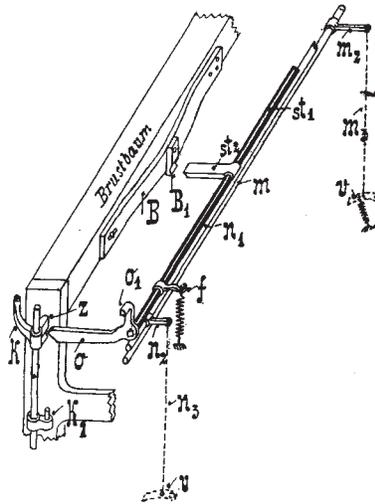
Ausrückung an Buckskestühlen durch die Bufferwelle.
